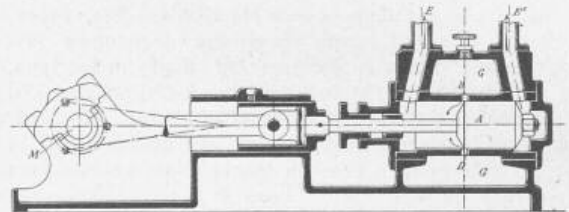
Hydraulische Steuerung von *Bonjour* an der dreistufigen Schiffsmaschine. — Triebcylinder.
